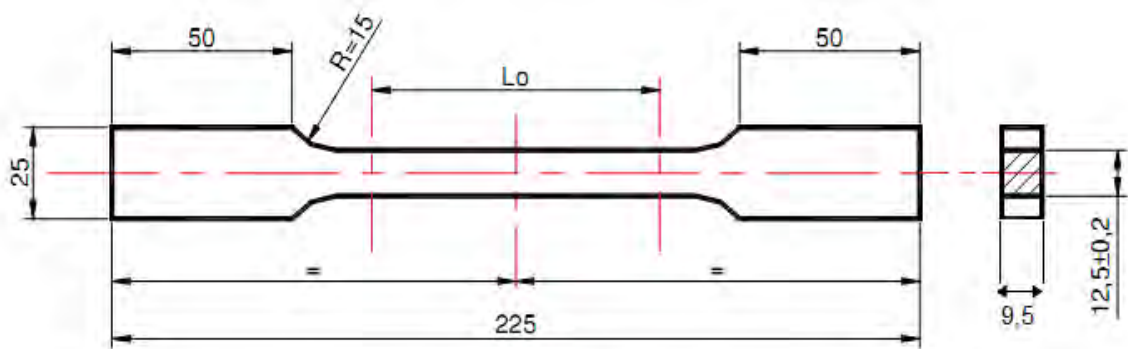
Representação geométrica e dimensional do corpo-de prova de tração plano.
